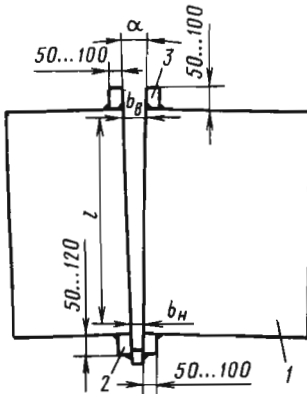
Общий вид стыка, подготовленного к ЭШС:
